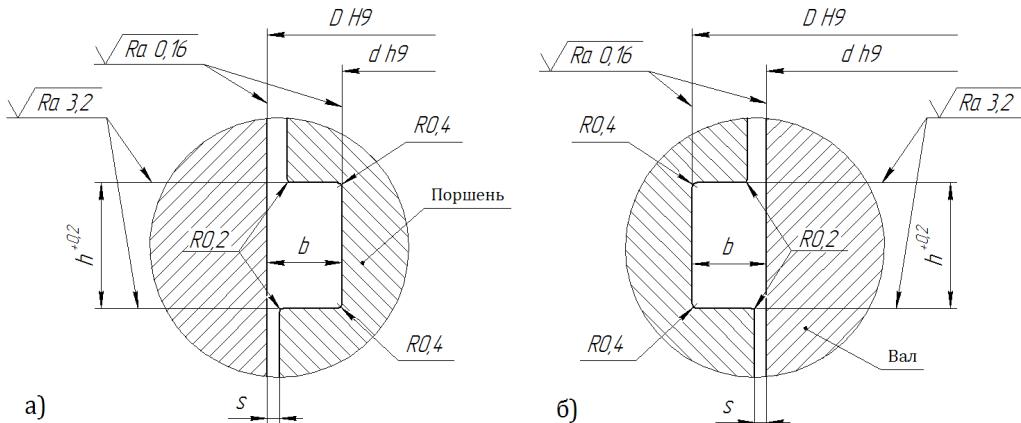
Закрытые канавки для уплотнения: а – поршня, б – штока
